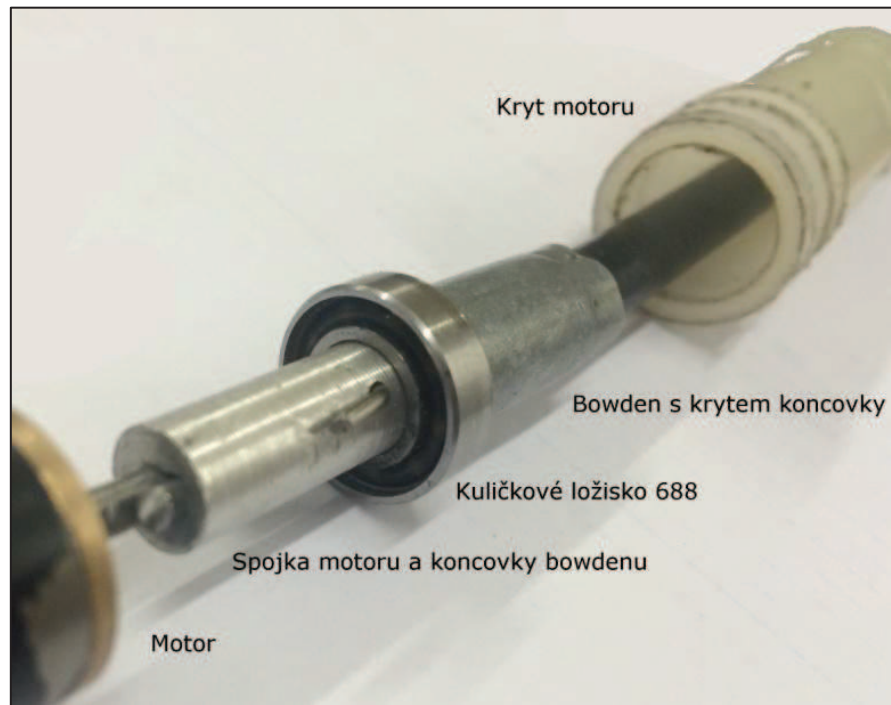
Kryt pro uchycení a zajištění motoru a koncovky bovdenu
